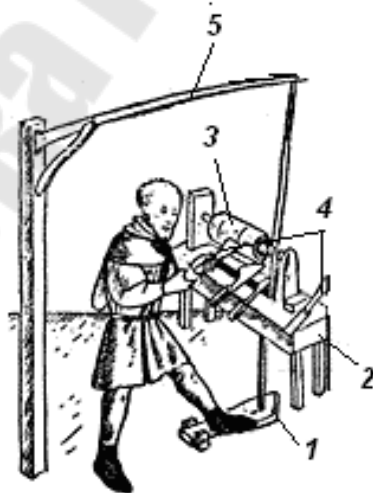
Эскиз токарного станка с педально-очеповым приводом: 1— педаль, 2— стойка с подручником, 3— заготовка, 4— резцы, 5— очеп
